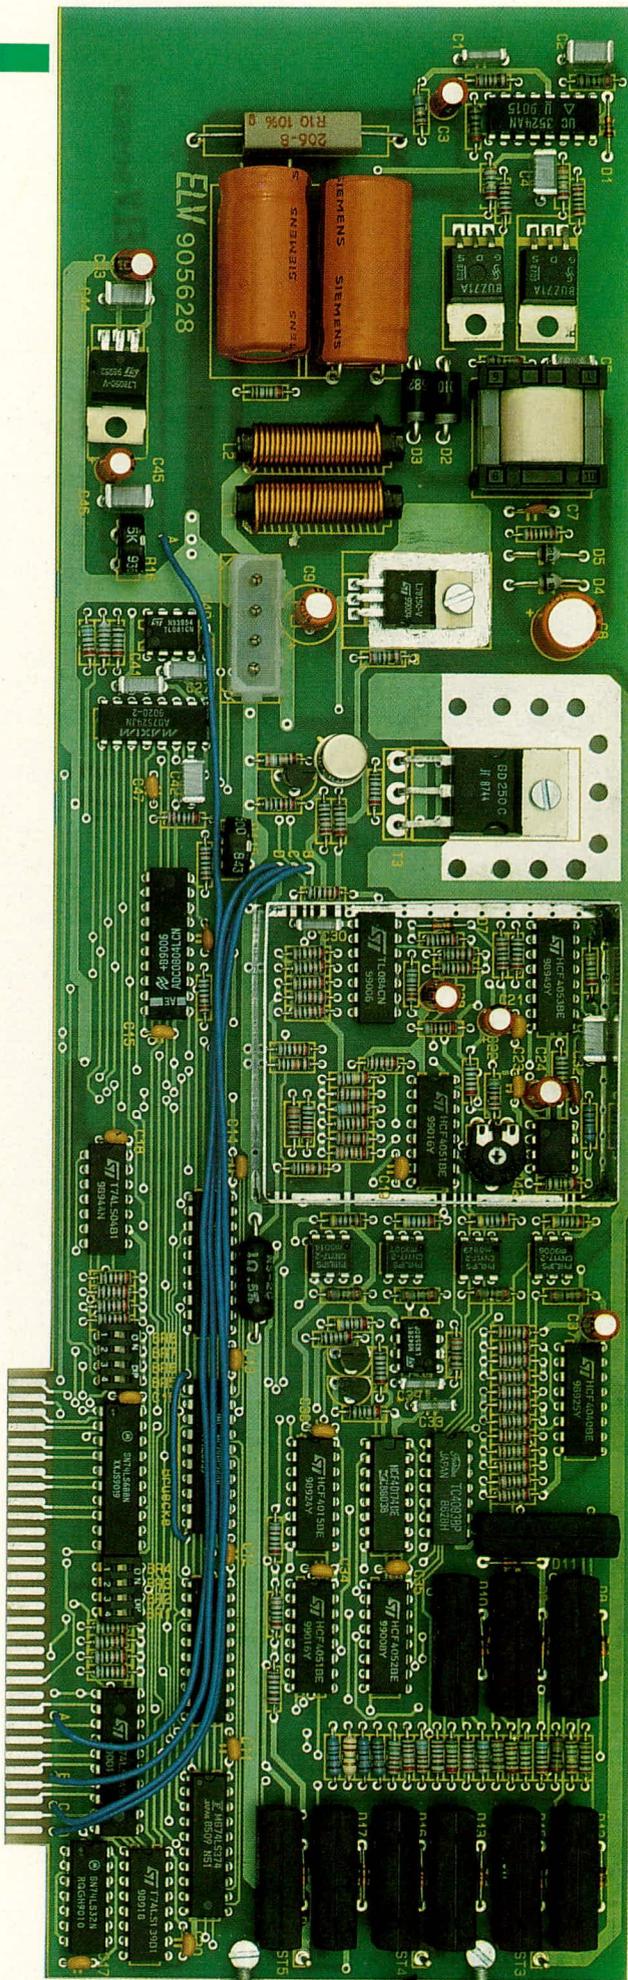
Ansicht des fertig aufgebauten PC-Transistortesters mit geöffnetem Abschirmgehäuse
